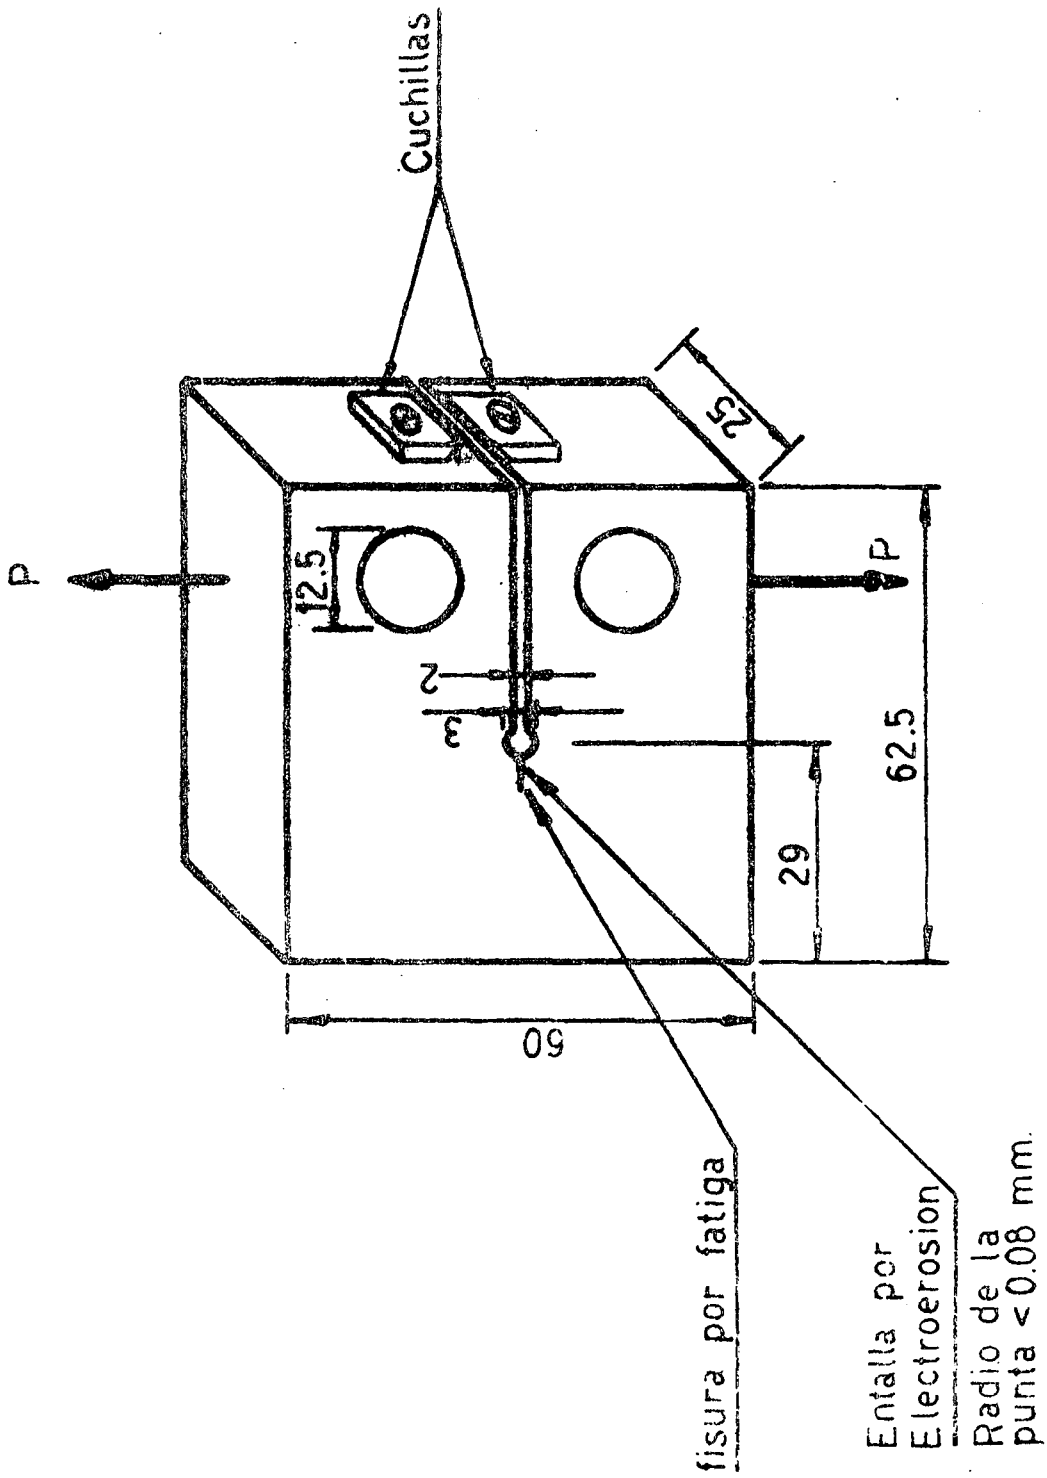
Probeta "compacta" con entalla "ojo de cerradura" y sus dimensiones principales.
